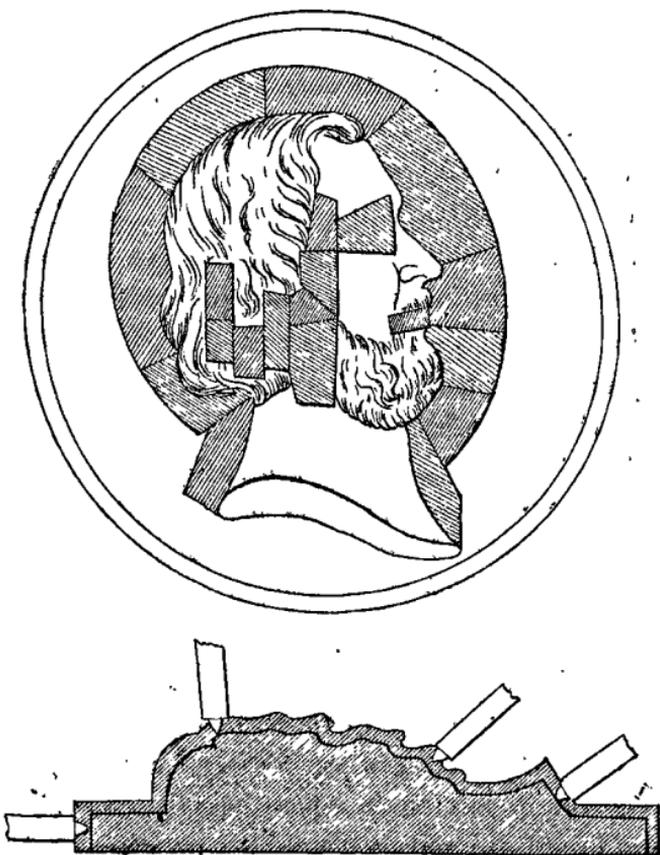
→ Moulage d'un médaillon avec pièces battues.
